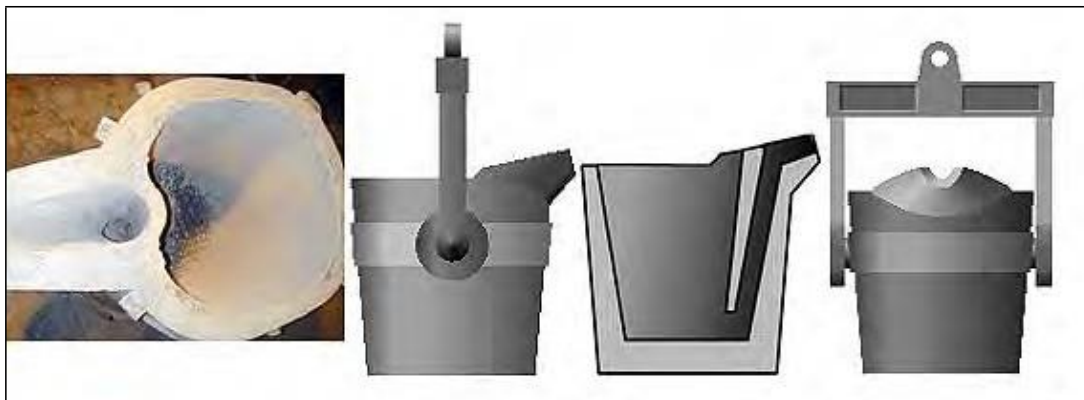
Ківш чайникового типу для заливання розплавленого металу
